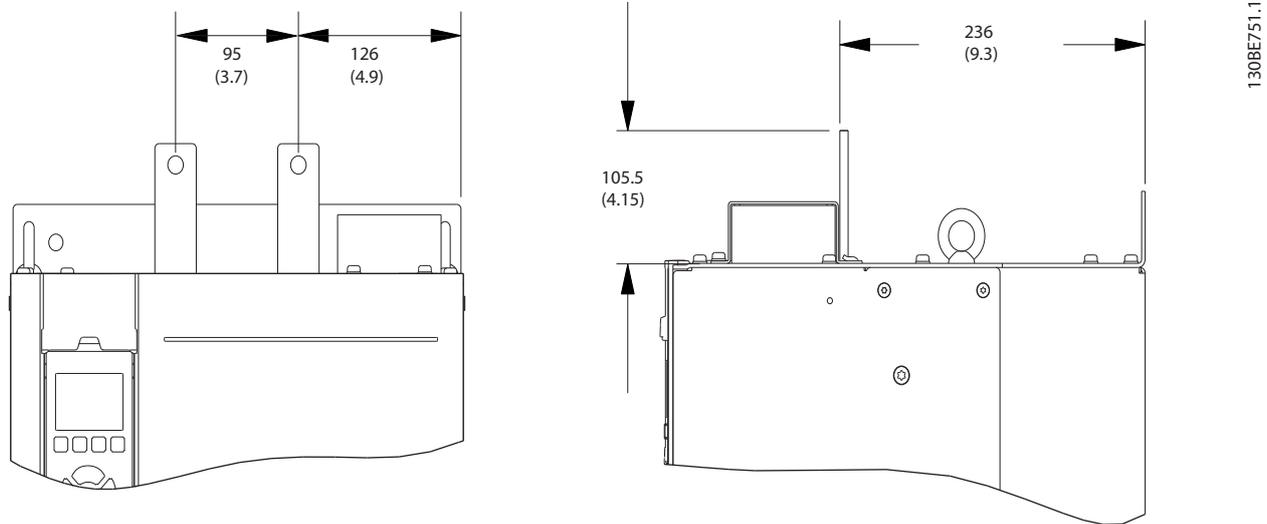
Dimensions du bus CC (vues avant et latérales)
